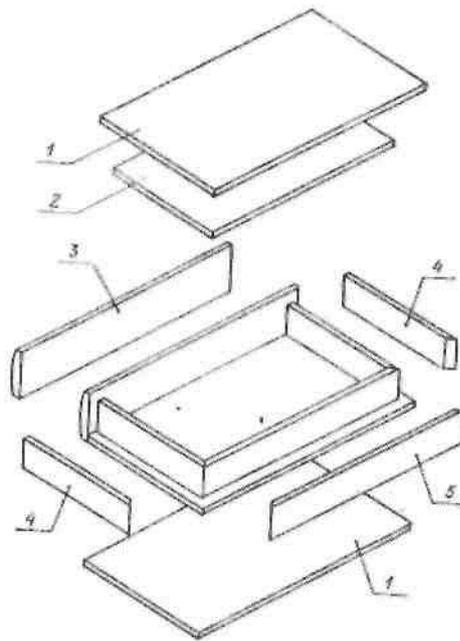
Шкатулка-книга: 1 - "корочки" (2 шт.); 2 - направляющая крышки (приклеивается к детали 1); 3 - "корешок"; 4 - боковые стенки ("страницы"); 5 - передняя стенка.
